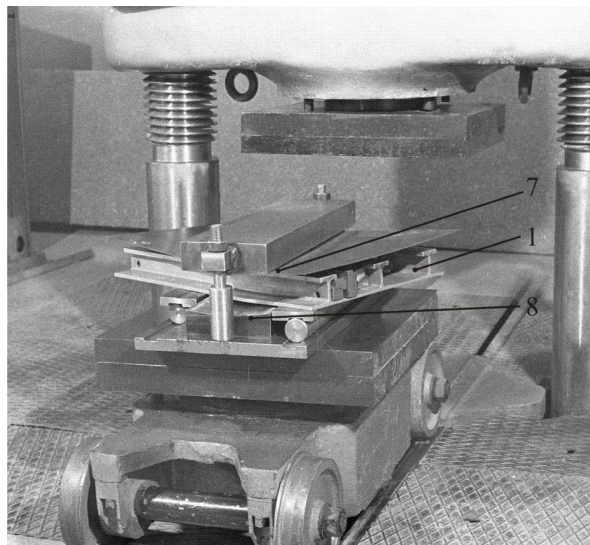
Внешний вид штампа для формовки с использованием оправки
